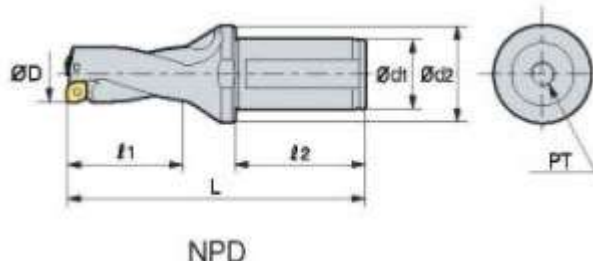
Чертеж и таблица размеров сборного сверла с СМП
